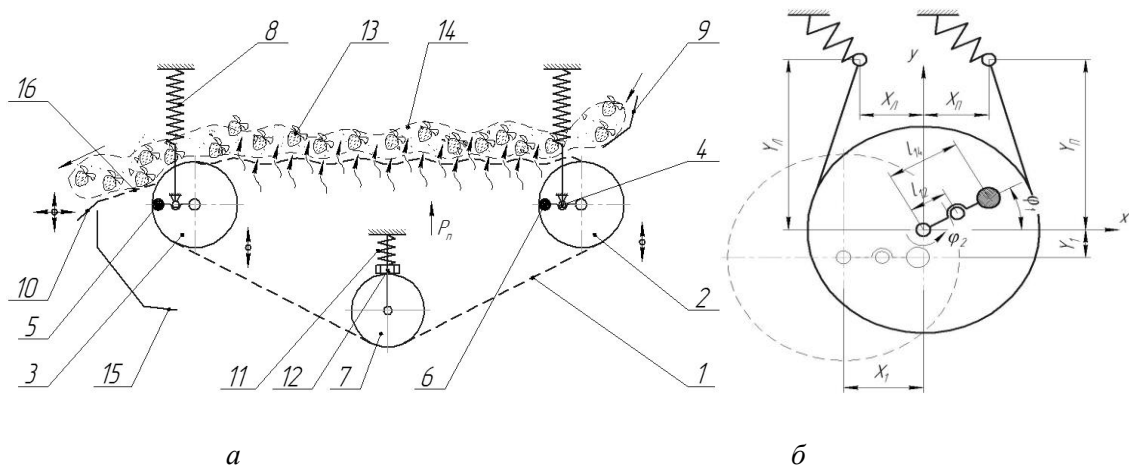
Принципова схема розробленої віброхвильової семіфлюїдизаційної машини(а): 1 – гнучка вантажонесуча стрічка; 2, 3 – робочі опорні вальці; 4 – приводний вал віброзбуджувача; 5, 6 – противаги; 7 – натяжний валець; 8 – пружна підвіска; 9, 10 – живильний та розвантажувальний лотки; 11 – пружний елемент натяжного пристрою; 12 – регулювальна гайка; 13 – продукція; 14 – холодоносій; 15 – лоток для відведення часток снігової шуби; 16 – вібраційний просівач; б – геометричні параметри приводу: X_1 – лінійне горизонтальне відхилення центра мас вальця; Y_1 – лінійне вертикальне відхилення центра мас вальця; φ_1 – кутове відхилення вальця; φ_2 – кутове відхилення центра мас приводного валу віброзбуджувача
